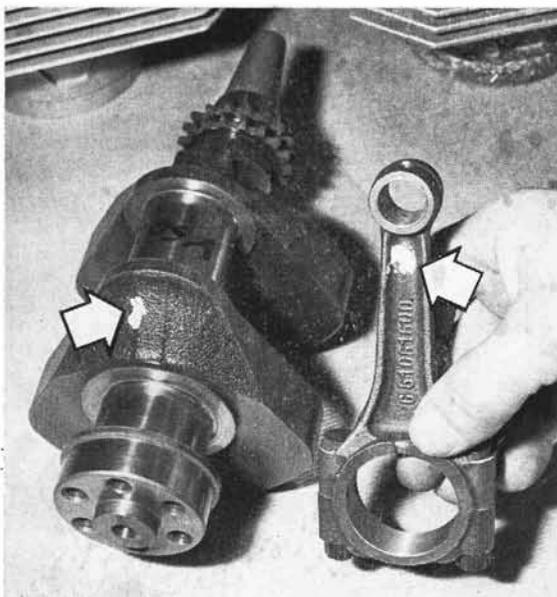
Appariement bielle-vilebrequin par touches de peinture (Photo RMT)
